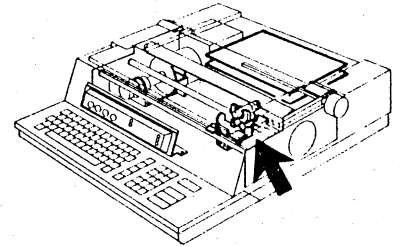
Assieme Testina e Carrello - Figure 9-3 Head and Carriage Assembly
